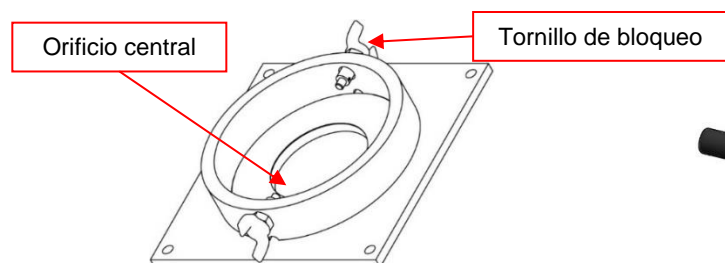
Montaje de la placa base giratoria (Mostrado P/N: 5074601)
